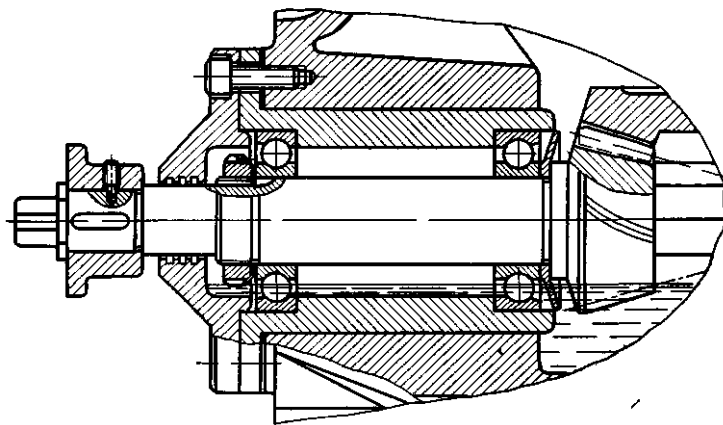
Установка радиально-упорных шарикоподшипников по схеме 4 – растяжку; обе опоры фиксирующие, крышка торцовая, регулирование подшипников - круглой илицевой гайкой.
